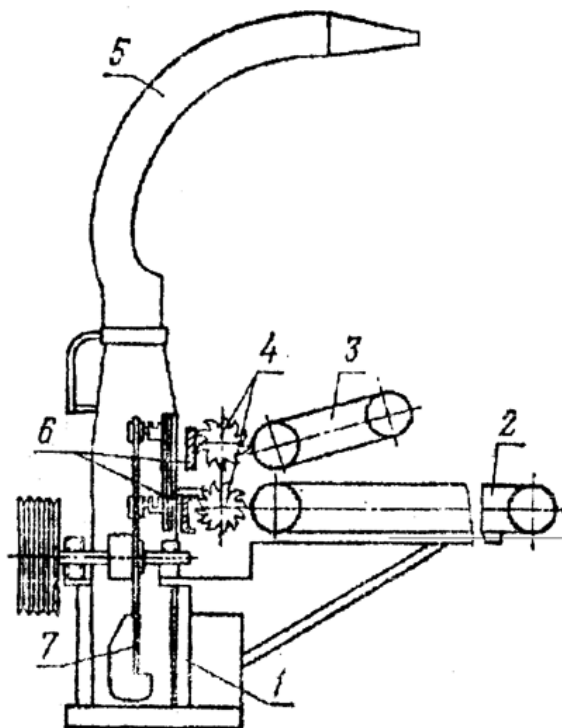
Схема соломорізки РСС-6Б: 1-рама; 2-транспортер; 3-підпресовуючий транспортер; 4-вальці; 5-дефлектор; 6-протиризальна пластина; 7- диск з ножами і лопатями» [4].
